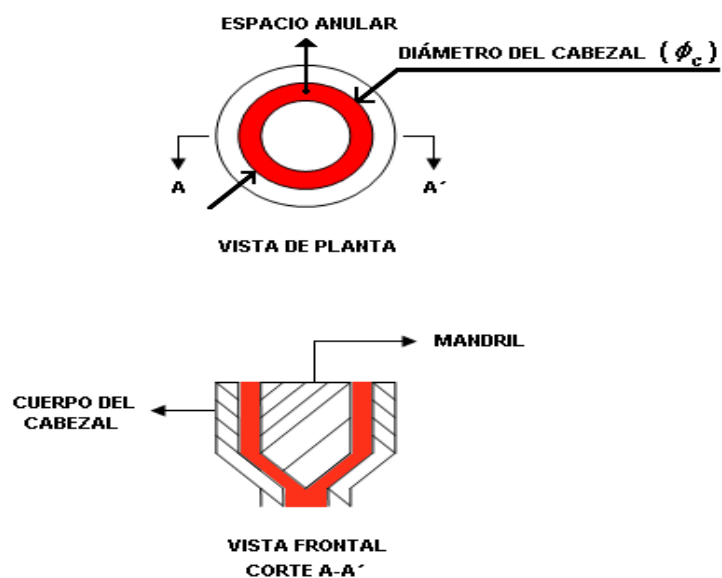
CABEZAL DE EXTRUSIÓN
